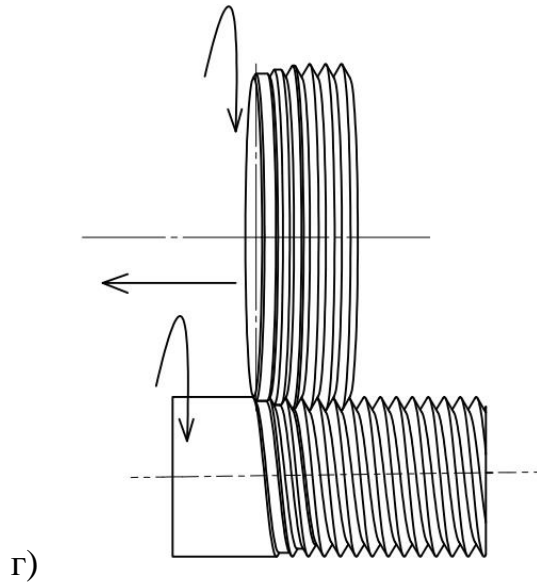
Методи оброблення різьби одно-, дво- та багатонитковими кругами
